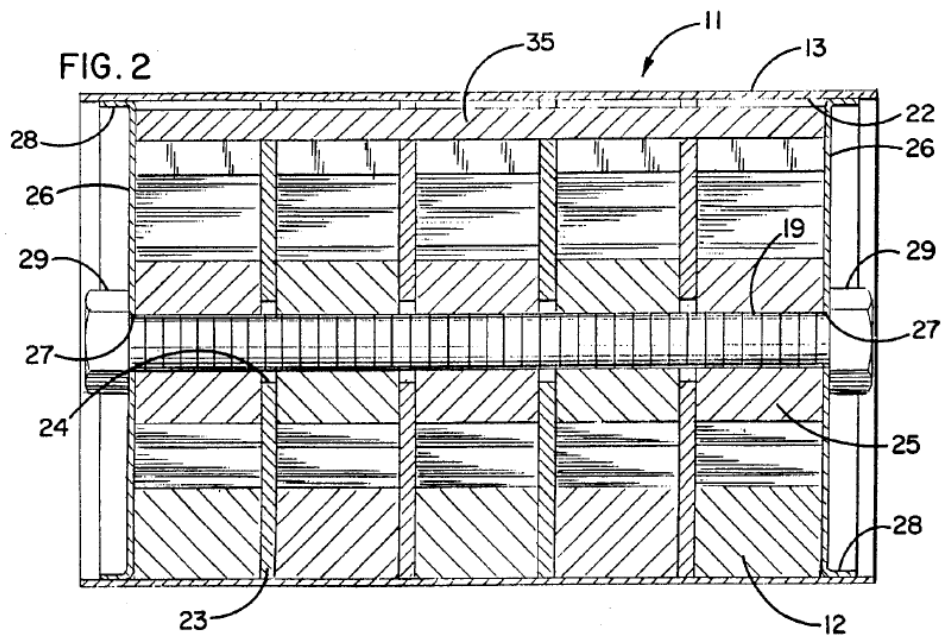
Magnetický roštový separátor firmy Sollau [12]
